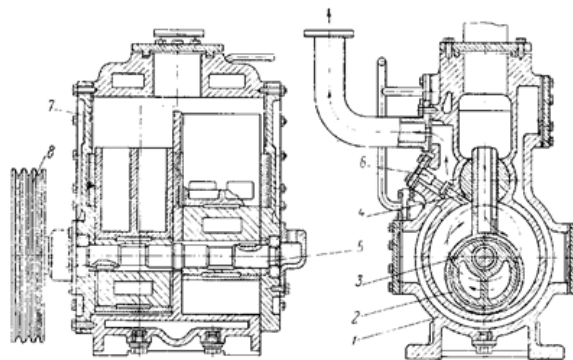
Двухступенчатый компрессор с катящимся ротором
